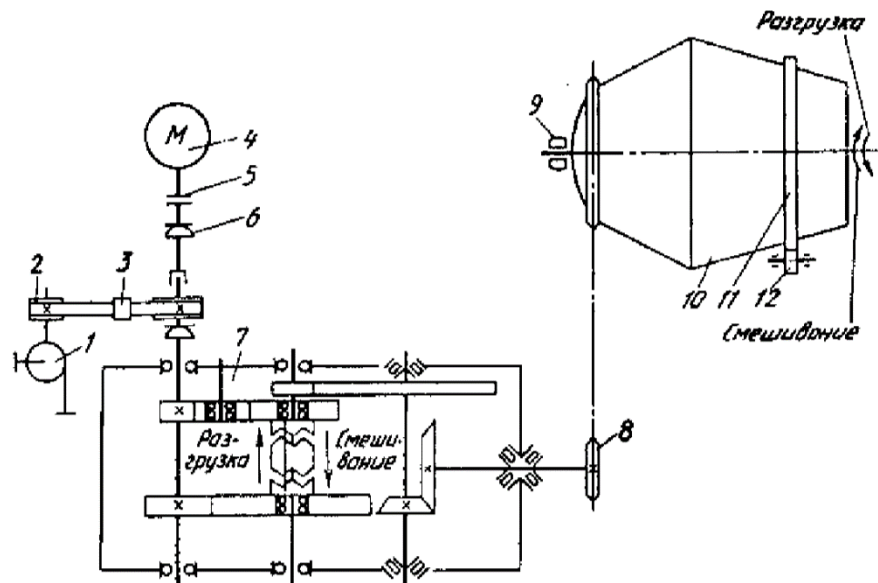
Кинематическая схема автобетоносмесителя: 1 - насос для подачи воды; 2 - ведомый шкив; 3 - натяжной ролик; 4 - двигатель; 5 - муфта сцепления; 6 - карданный вал; 7 - редуктор; 8 - цепная передача; 9 - главный опорный подшипник, 10 - барабан; 11 - бандаж; 12 - опорный ролик
